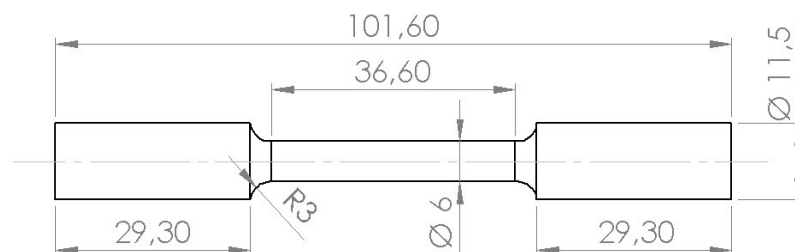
Dimensões nominais (mm) dos corpos de prova para ensaio de tração.
